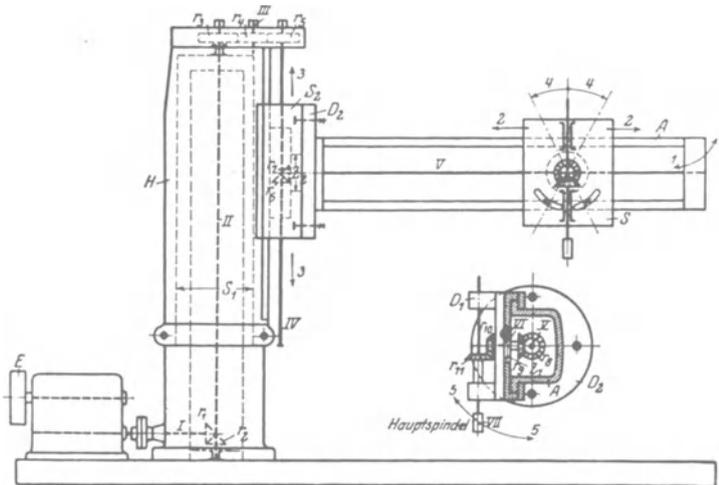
Antrieb der nach 5 Richtungen einstellbaren Hauptspindel. (Auslegerbohrmaschine.)
